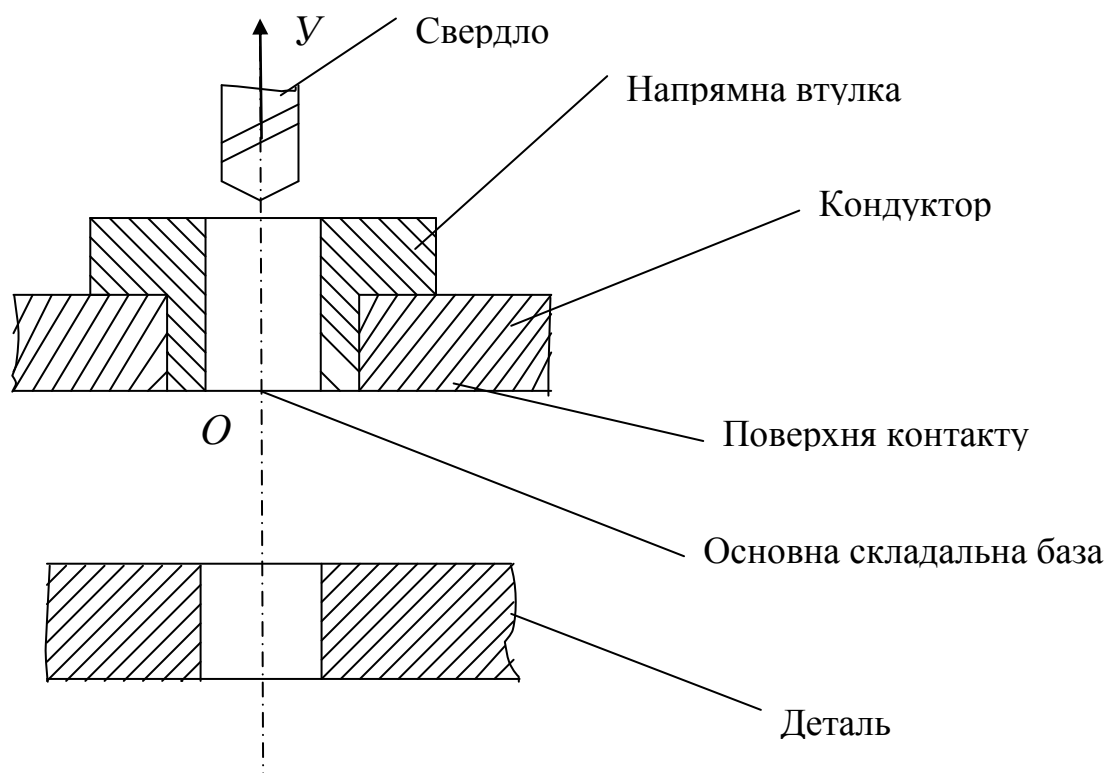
Прив'язка системи координат направляющего приспособления
